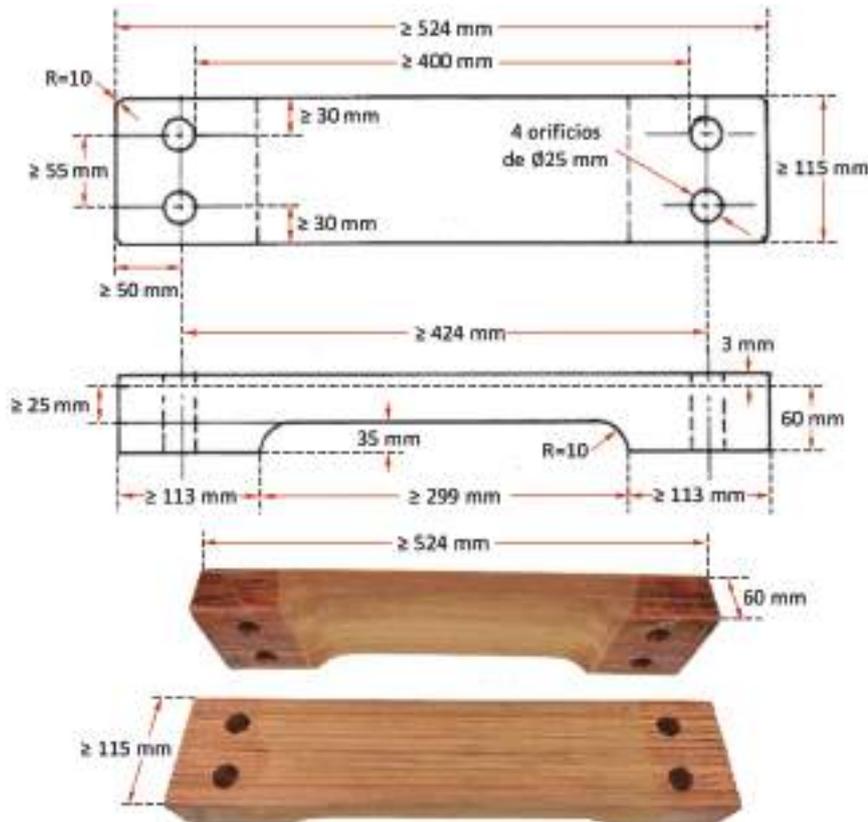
Dimensiones de los peldaños diseñados para carretel mecánico.
